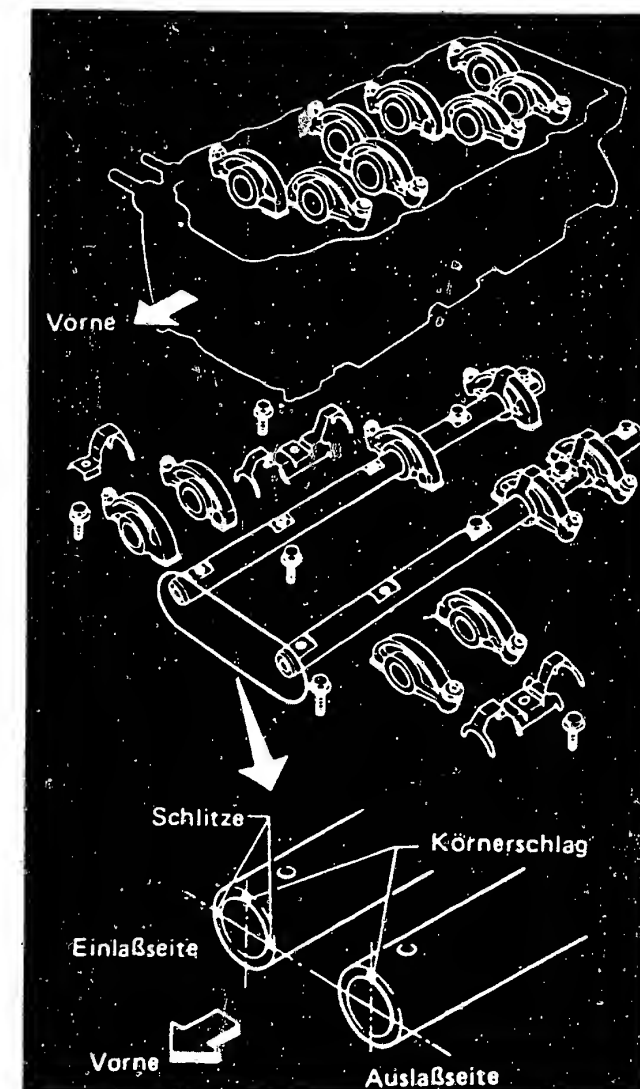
Beim Einbau der Kipphebel sind die Schrauben bereits in die Bohrungen auf den Wellen einzusetzen, damit die Federn nicht abrutschen können.
